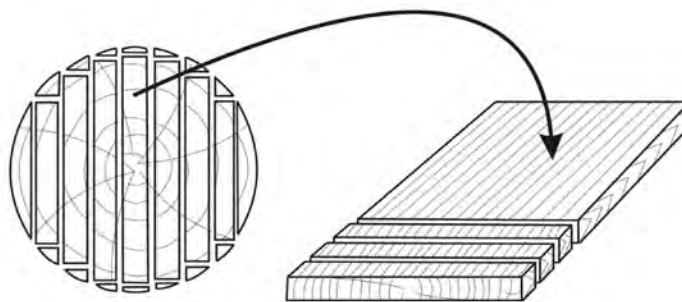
Раскрой бревна и доски для изготовления древесной заготовки
